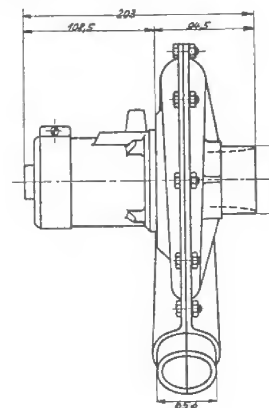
Scintilla-Elektro-Anfachgebläse Typ HKR
